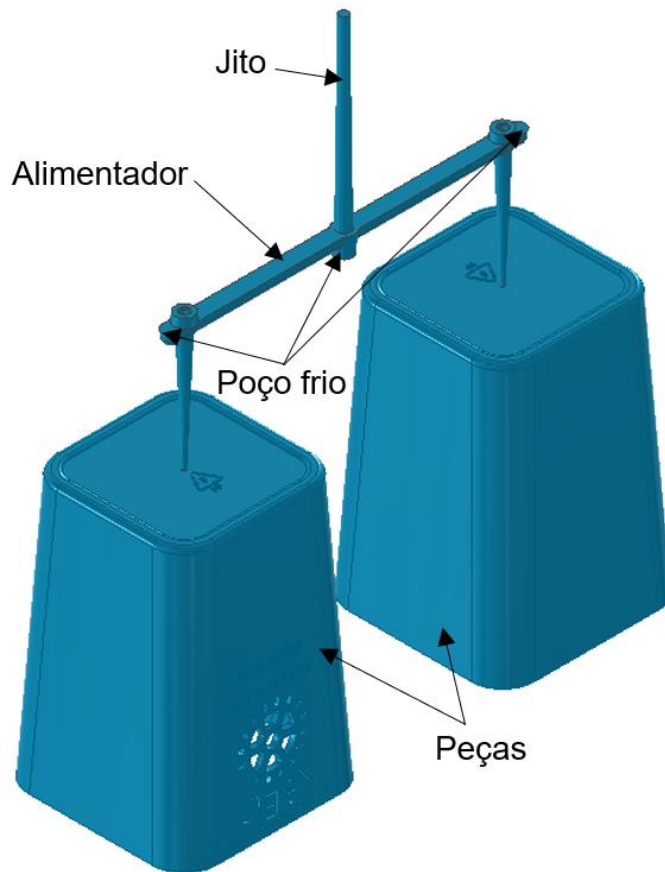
Representação do sistema de injeção e as peças moldadas.
